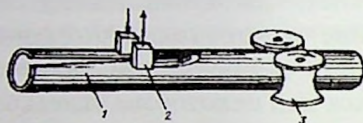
Схема кондуктивного токоподвода при непрерывной высокочастотной стыковой сварке:
